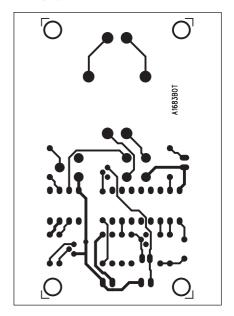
Obrazec desky spojů senzoru (strana TOP)
